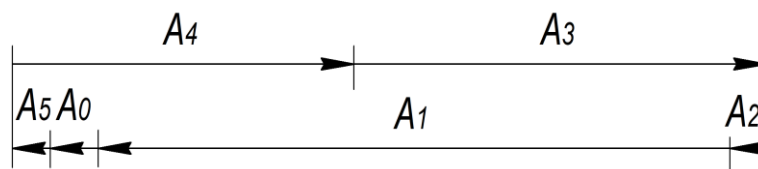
Розмірний ланцюг роз'ємного корпусу
